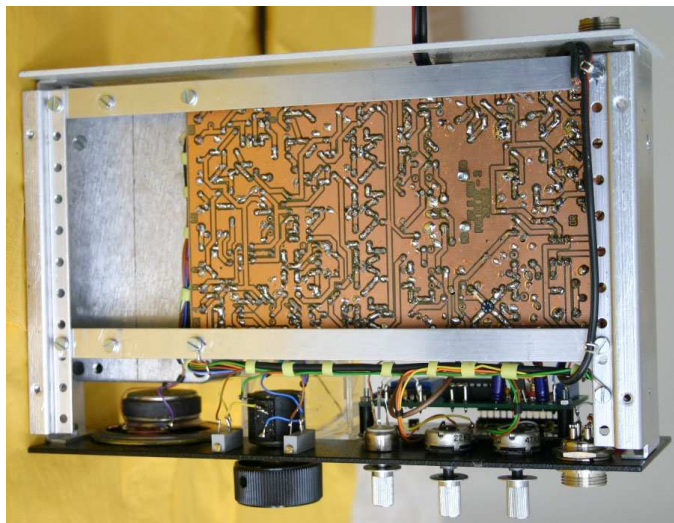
Ansicht des aufgebauten Gerätes von unten
